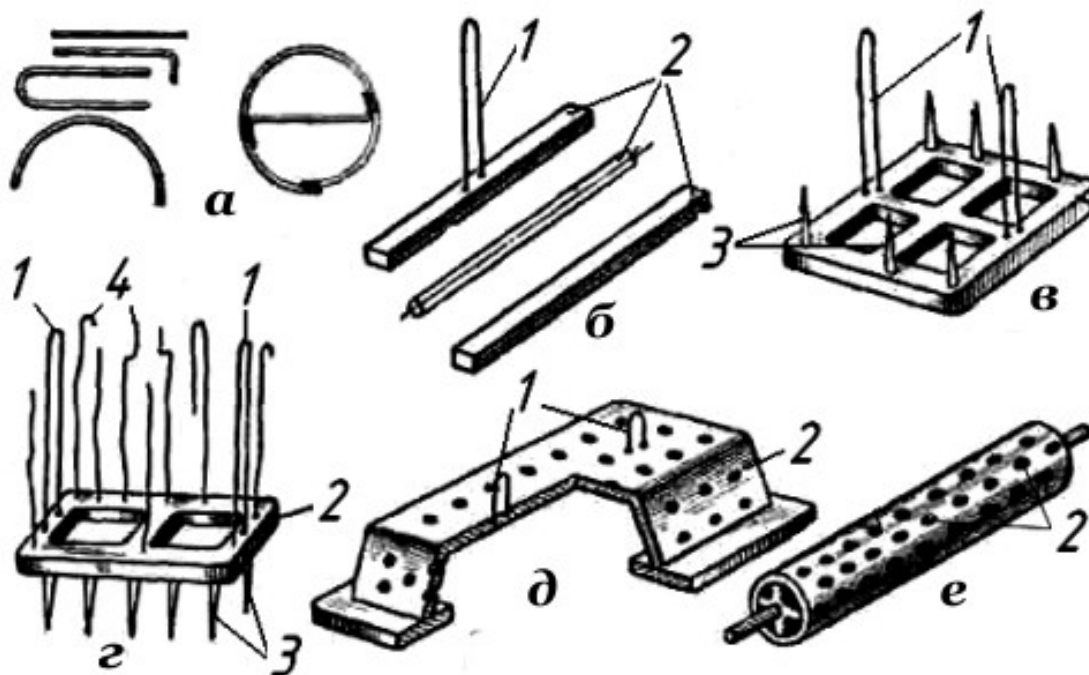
Стержневые каркасы: а — проволочные; б — сварные планки; в — рамочные литые чугунные; г — комбинированные; д — коробчатые; е — трубчатые; 1 — подъемы; 2 — основания; 3 — шпильки; 4 — проволока
